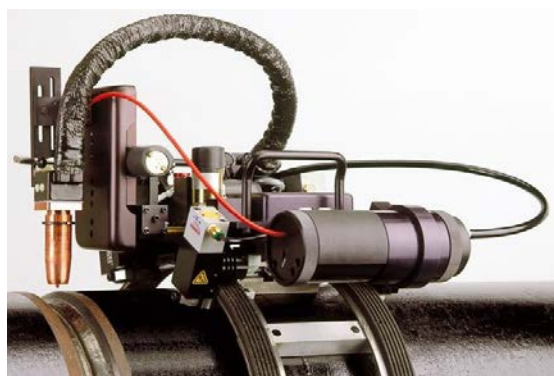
Установка для сварки PRD-100
